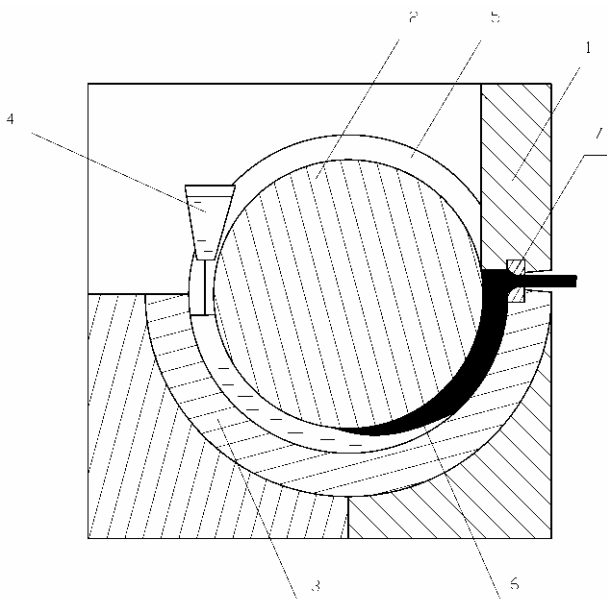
Устройство для непрерывного литья-прессования (Кастекс)
